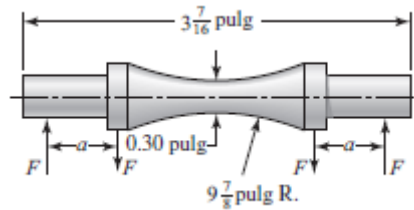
Máquina rotativa de R.R. Moore. Dimensiones estándares de una probeta para ensayo
